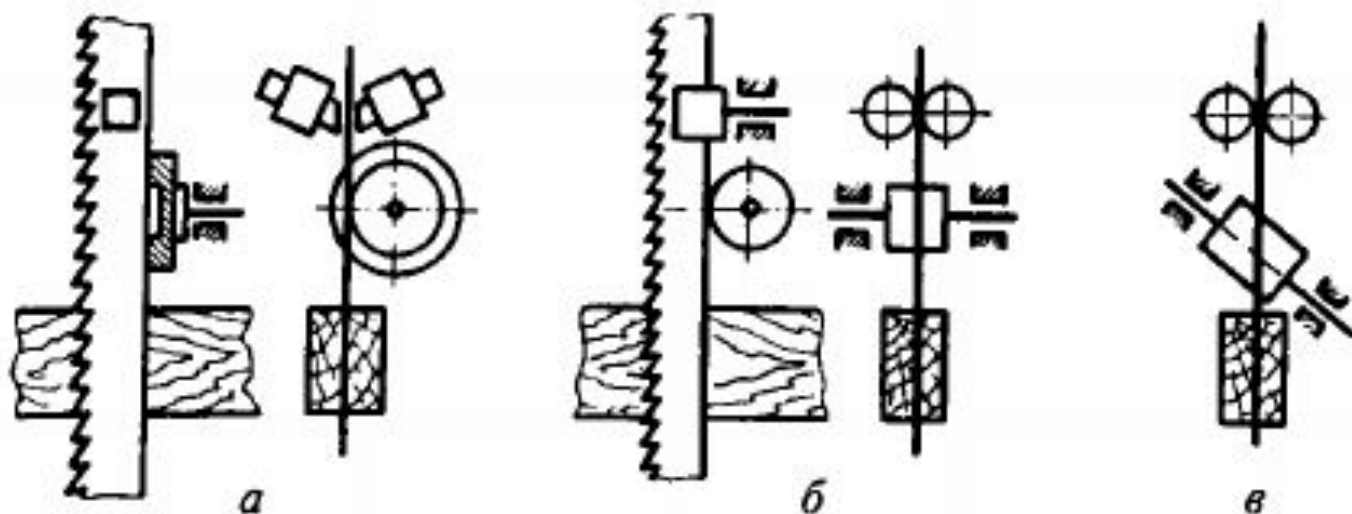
Схемы направляющих устройств для рабочей (сбегающей) ветви ленточной пилы:
